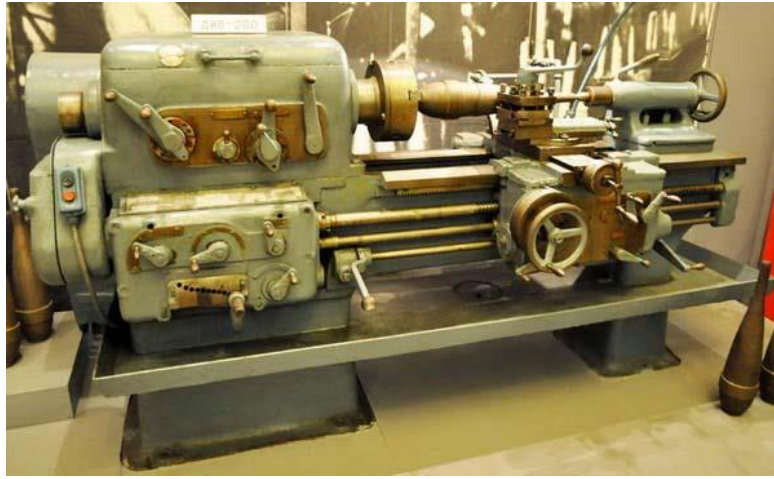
Перша модель токарно-гвинторізного верстата ДПП
